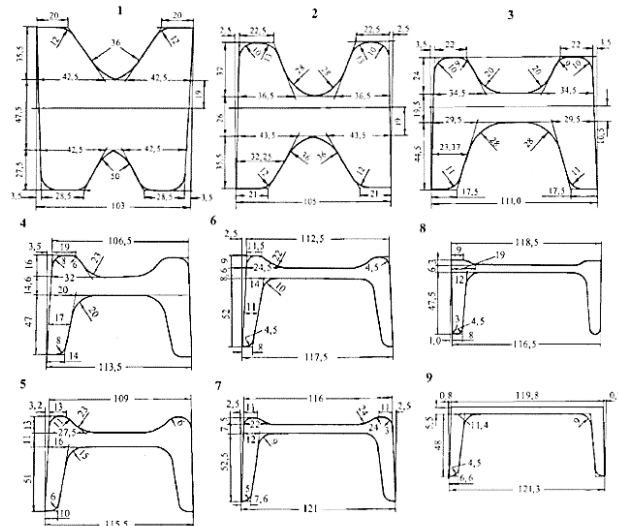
Калибровка валков для прокатки швеллера №12 прямополочного типа балочного подтипа с малым уклоном и одним контрольным калибром, ТСК 1111 [18]
